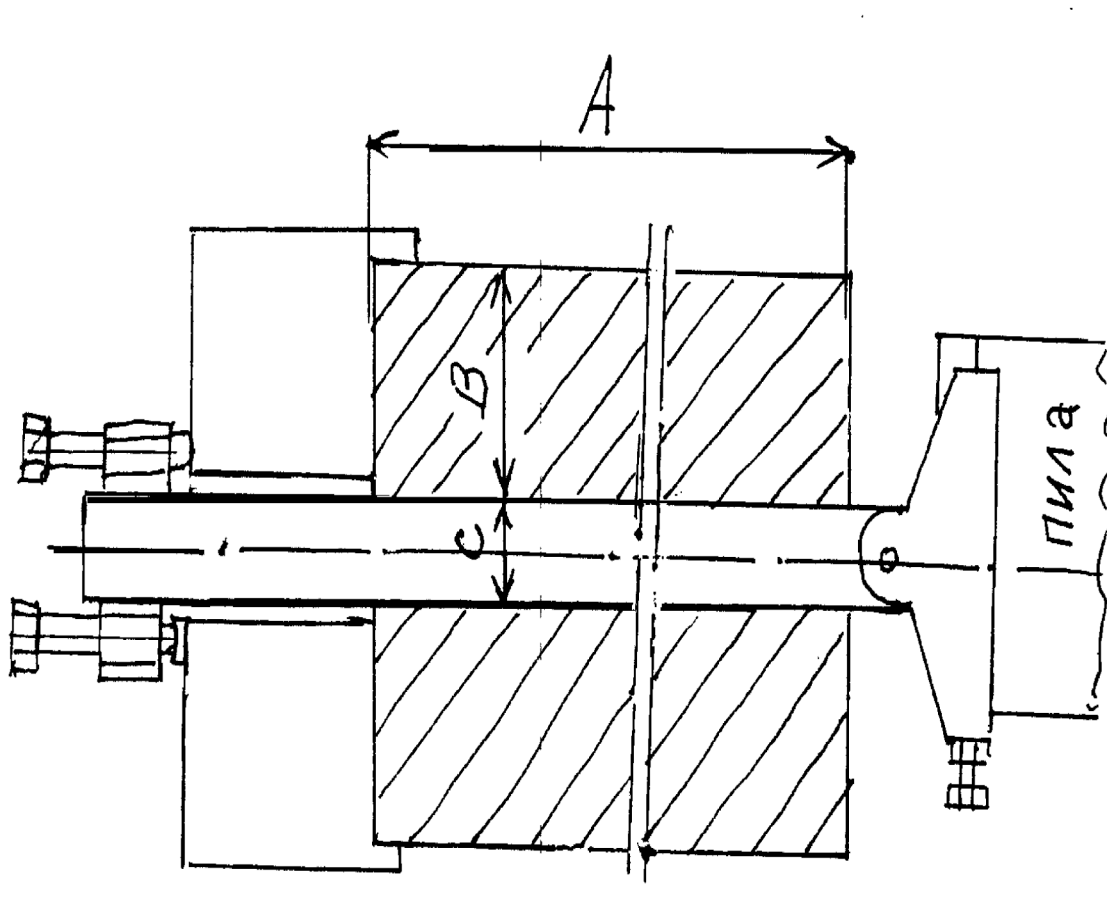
Приспособление для механического натяжения пилы
